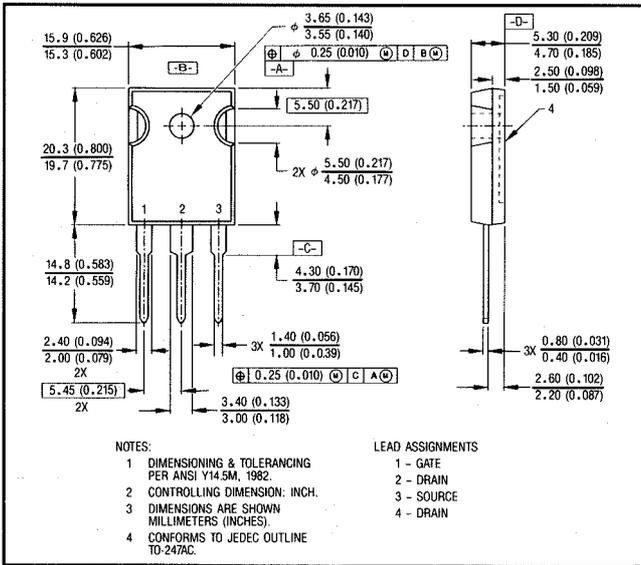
Стандартный пластмассовый корпус TO-247 AC
